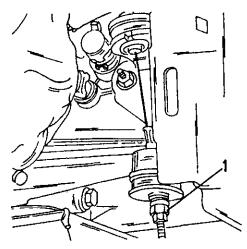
На двигателе типа TU педаль сцепления регулируется двумя гайками (1).
